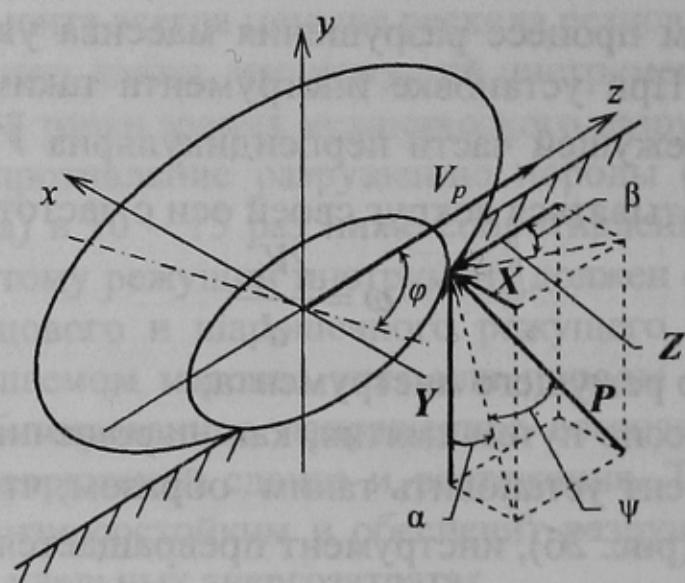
Схема усилий, формирующихся на режущем инструменте с вращающейся режущей кромкой при разрушении пласта.
